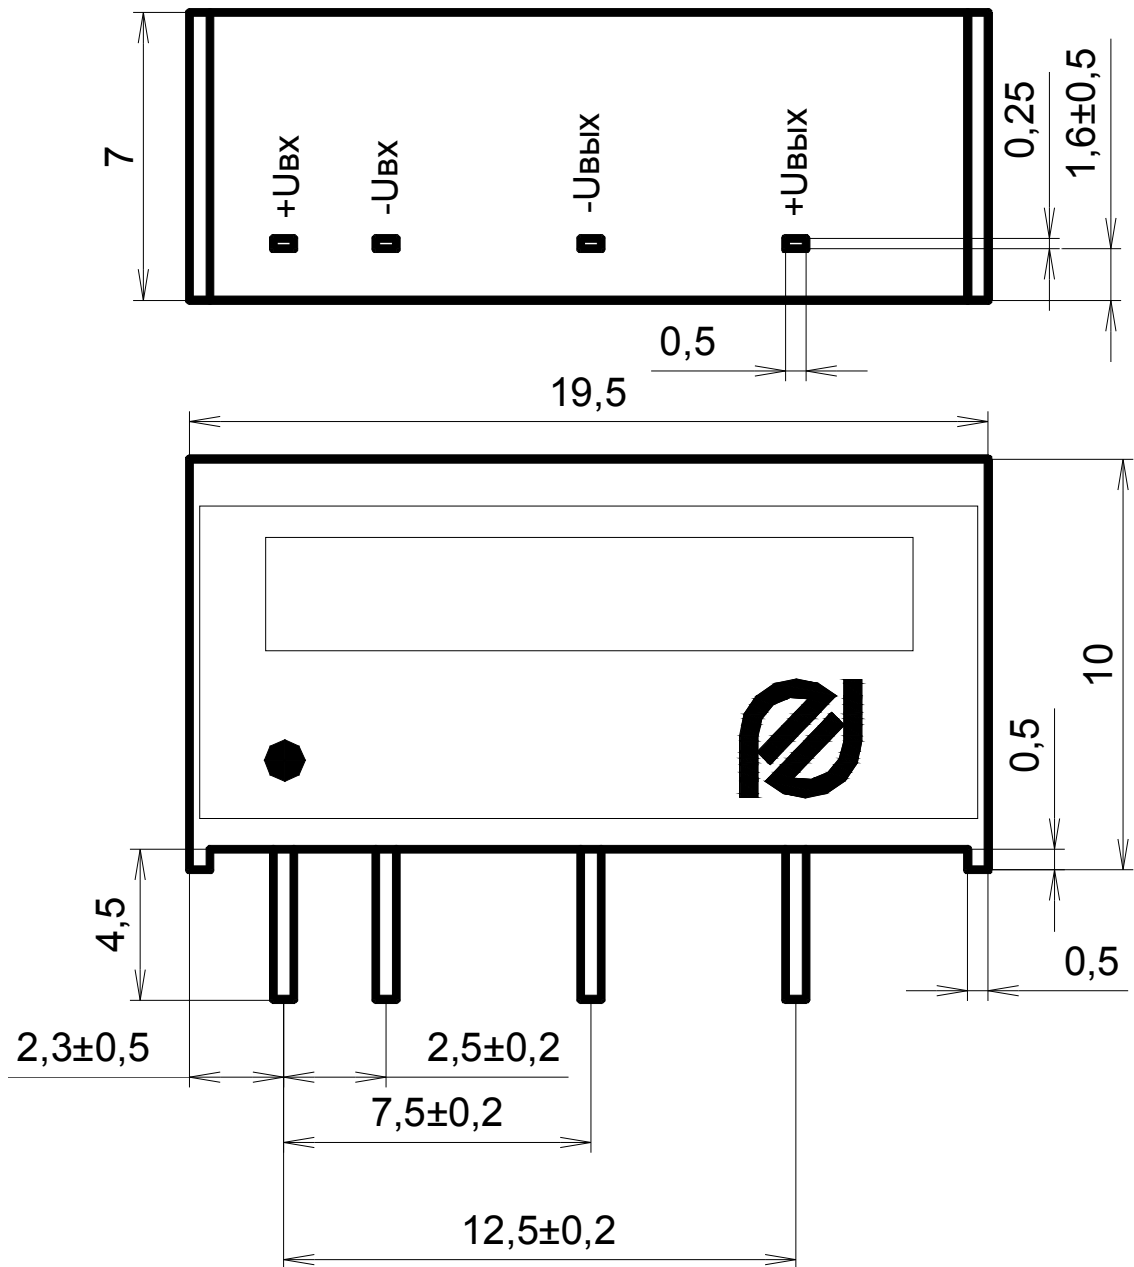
Габаритный чертеж модулей в корпусе «Н»
